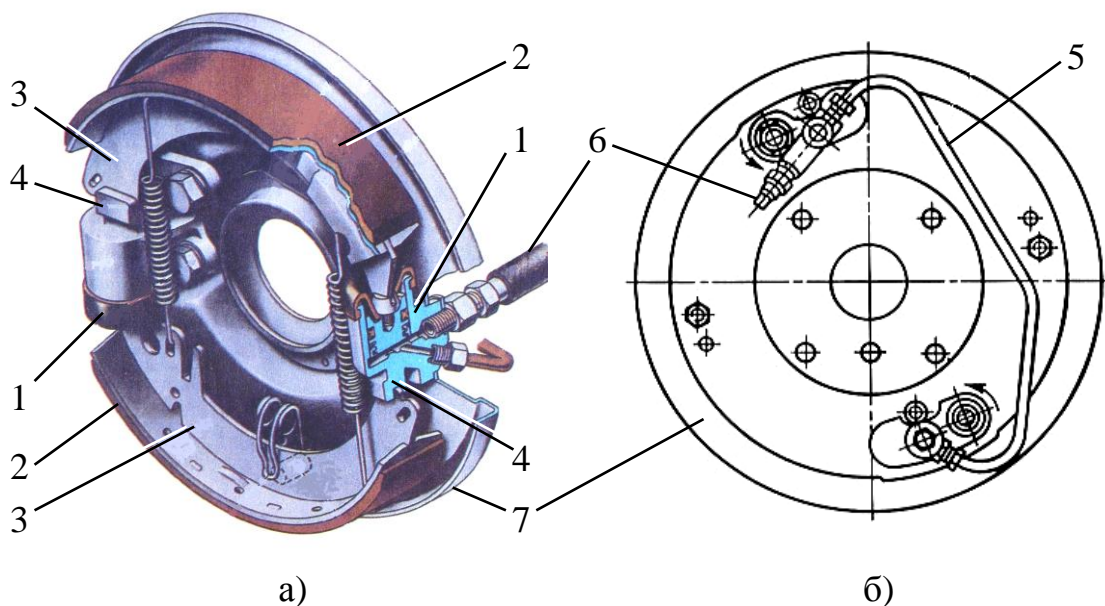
Барабанный тормозной механизм с равными приводными силами и разнесенными опорами: а – конструкция, б – вид с обратной стороны на опорный неподвижный диск тормозного механизма; 1 – разжимные устройства; 2 – накладки тормозных колодок; 3 – тормозные колодки; 4 – опоры колодок; 5 – соединительный трубопровод; 6 – подводящий трубопровод; 7 – опорный неподвижный диск тормозного механизма
